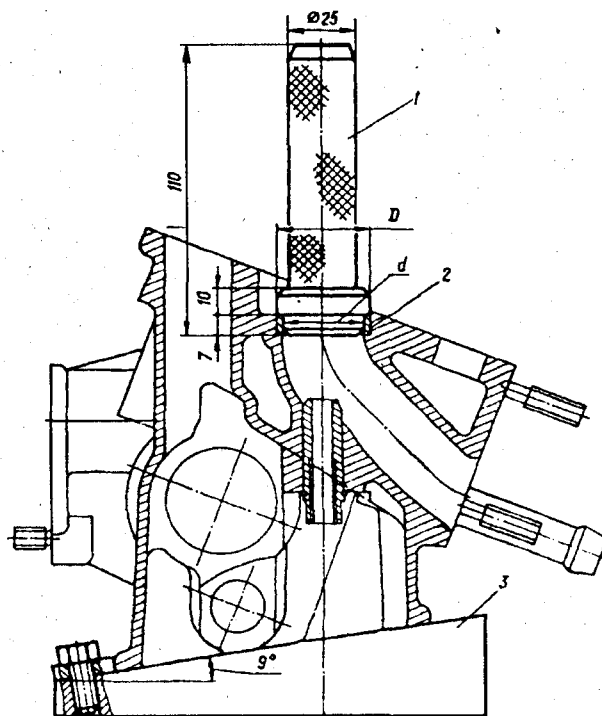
Оправки для запрессовки седел клапанов: 1 – оправка для седел выпускных и для седел впускных клапанов; 2 – седло клапана; 3 – подставка
